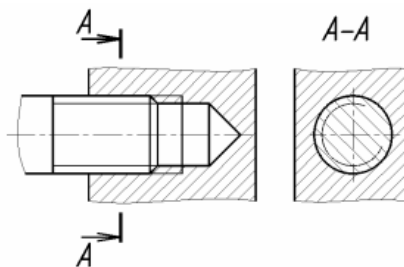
Изображение резьбы на разрезе резьбового соединения
